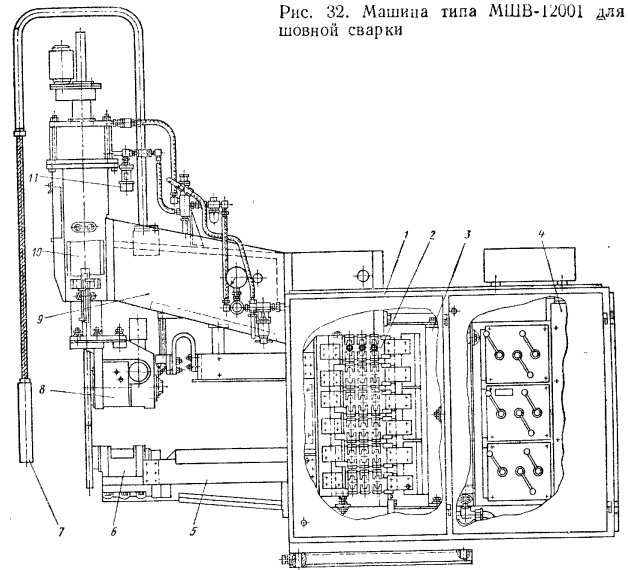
Машина типа МШВ-12001 для шовной сварки
